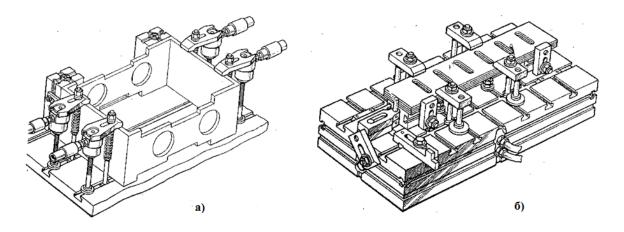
Приспособления с применением УСПМ – ЧПУ: а) приспособление для фрезерования пазов в детали типа коробка; б) приспособление для фрезерования пазов в детали типа сепаратора
